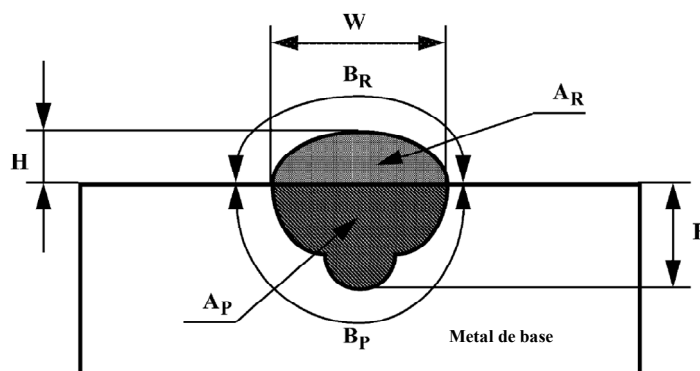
Parâmetros geométricos do cordão de solda.
